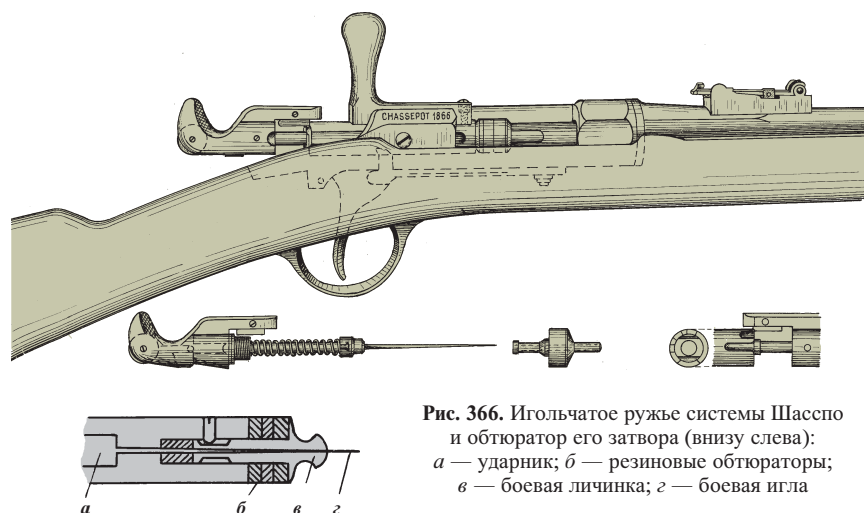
Игольчатое ружье системы Шасспо и obturator его затвора (внизу слева): а — ударник; б — резиновые obturаторы; в — боевая личинка; з — боевая игла
